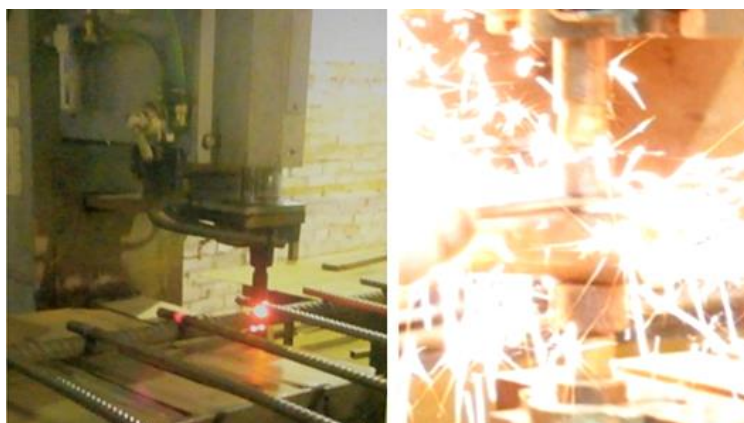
Сварка крестовых соединений арматуры
